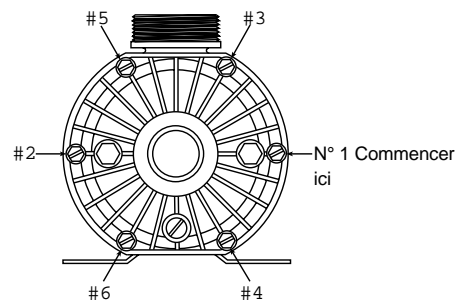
Ordre de serrage de la plaque avant de la pompe
